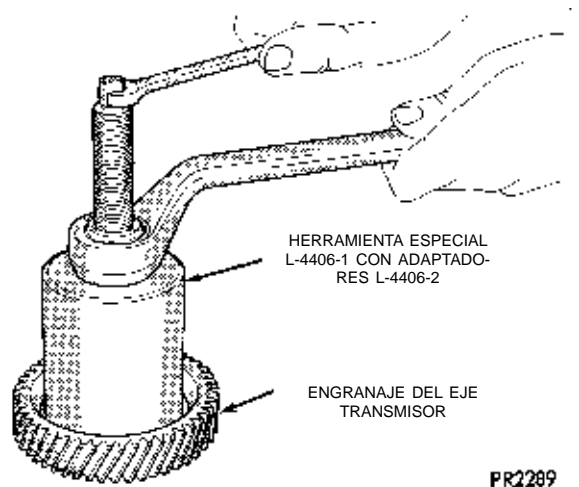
Desmontaje del cono de cojinete de engranaje del eje transmisor
